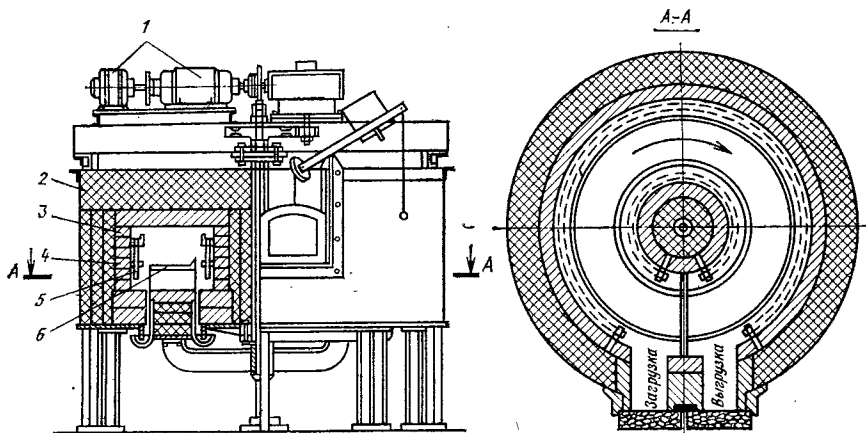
Карусельная электрическая печь: 1 — привод с редуктором; 2 — каркас печи; 3 — теплоизоляция; 4 — огнеупорная кладка; 5 — нагреватель; 6 — жароупорная плита
